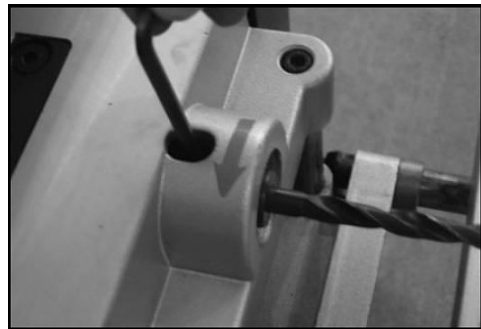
Passenden Adapter und Werkzeug einsetzen
